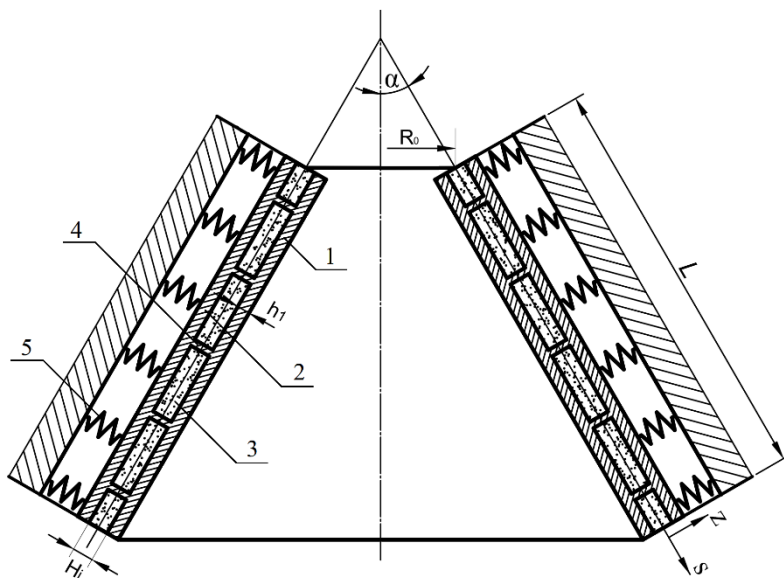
Конструкція тришарової конічної оболонки з полімерним заповнювачем
